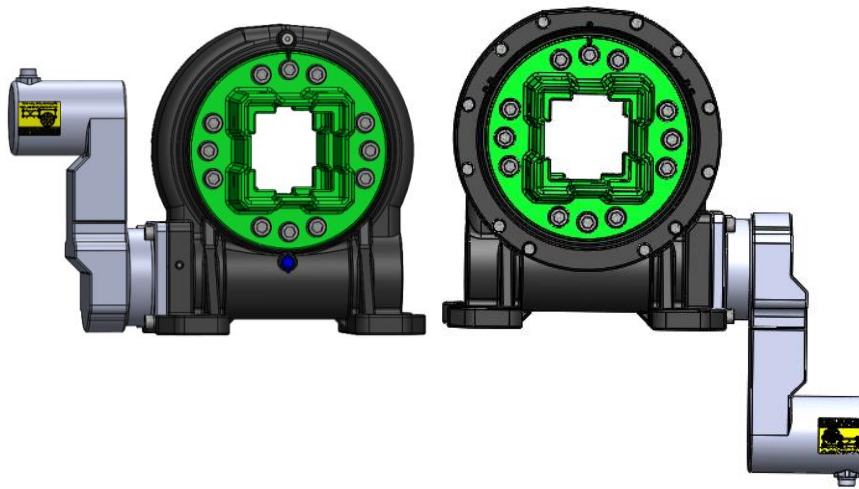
Posición de venta (izquierda); Posición de trabajo (derecha)
